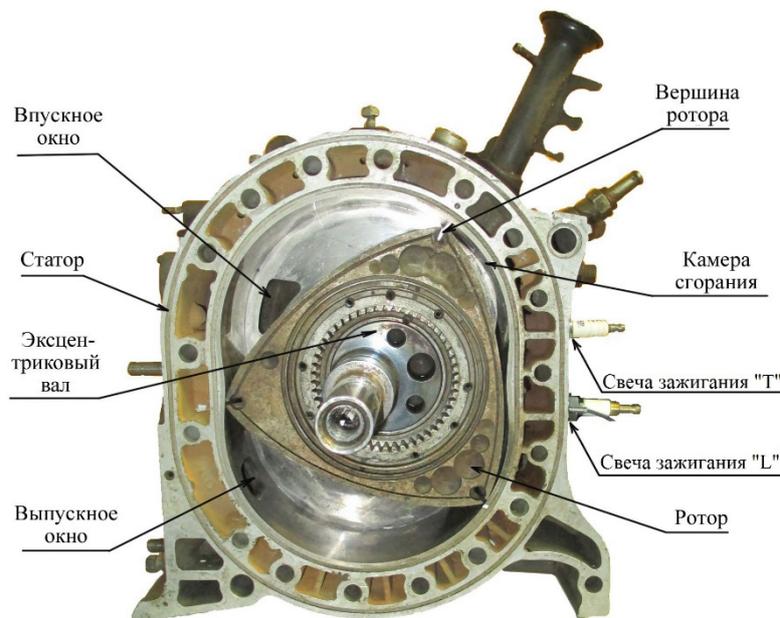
Роторный двигатель Ванкеля со снятой задней крышкой
